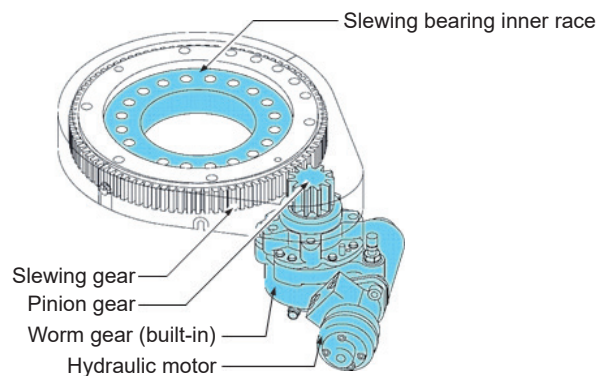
Mekanismo ng Crane na Trak Loader Slewing (Slewing Bearing Type)
